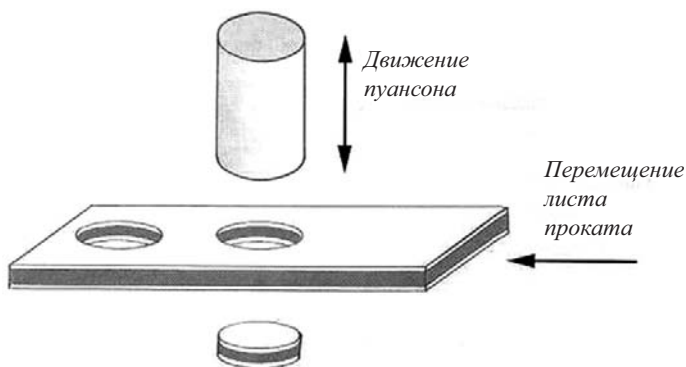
П. Схема вырубki биметаллических заготовок для монет
